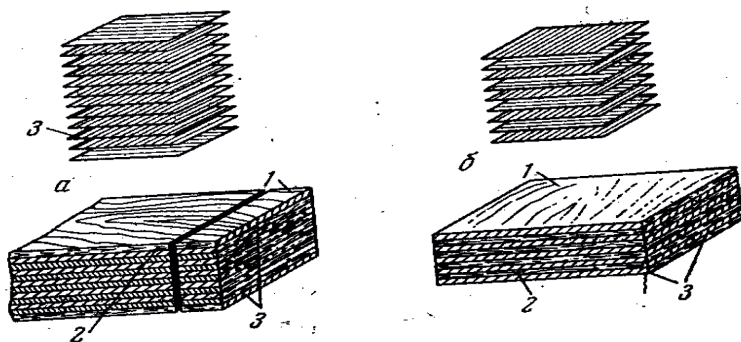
Схема расположения листов шпона в плитах древесного слоистого пластика: а – марки ДСП-Б; б – марки ДСП-В; 1 – плоскость прессования; 2 – ребро; 3 – торец
